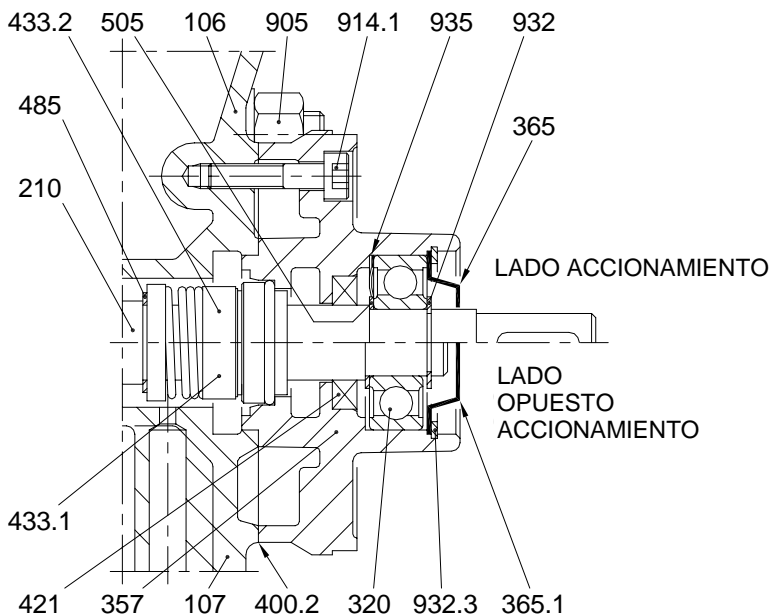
Diseño en sección del soporte de cojinete y del cierre mecánico
